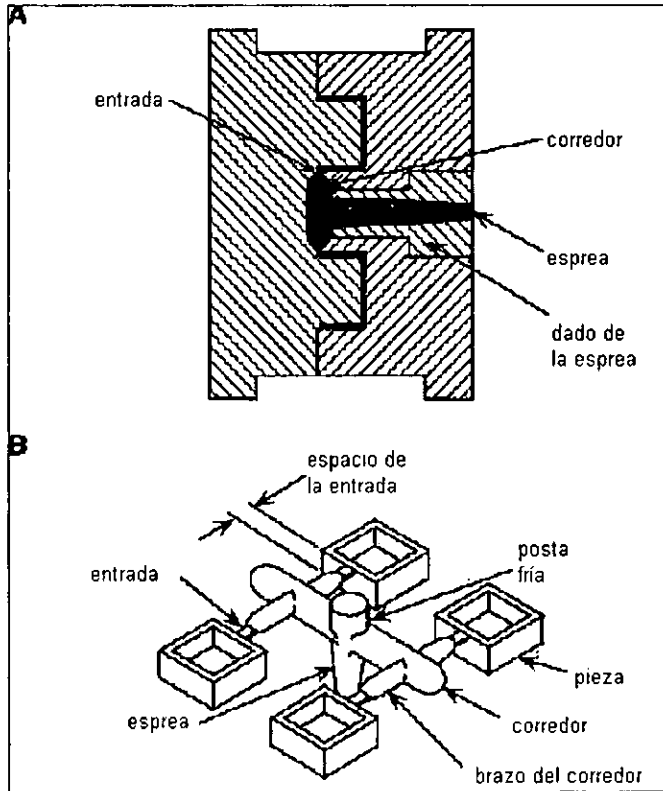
A. Modelo típico de molde usado en un proceso de moldeo por inyección de multiimpresión para la producción de cajas de plástico en este ejemplo. B. Pieza moldeada retirada del molde que muestra las cajas y el plástico de desecho¹⁸.
